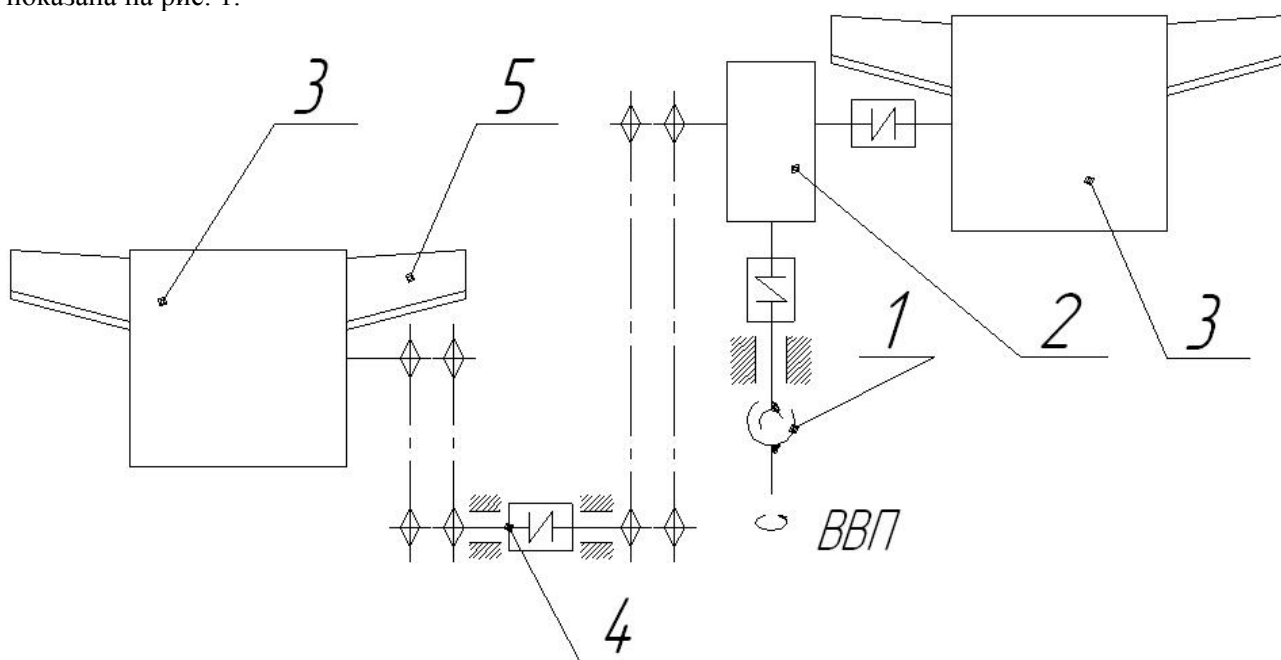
Кінематична схема привода плоскоріза з активними робочими органами:
